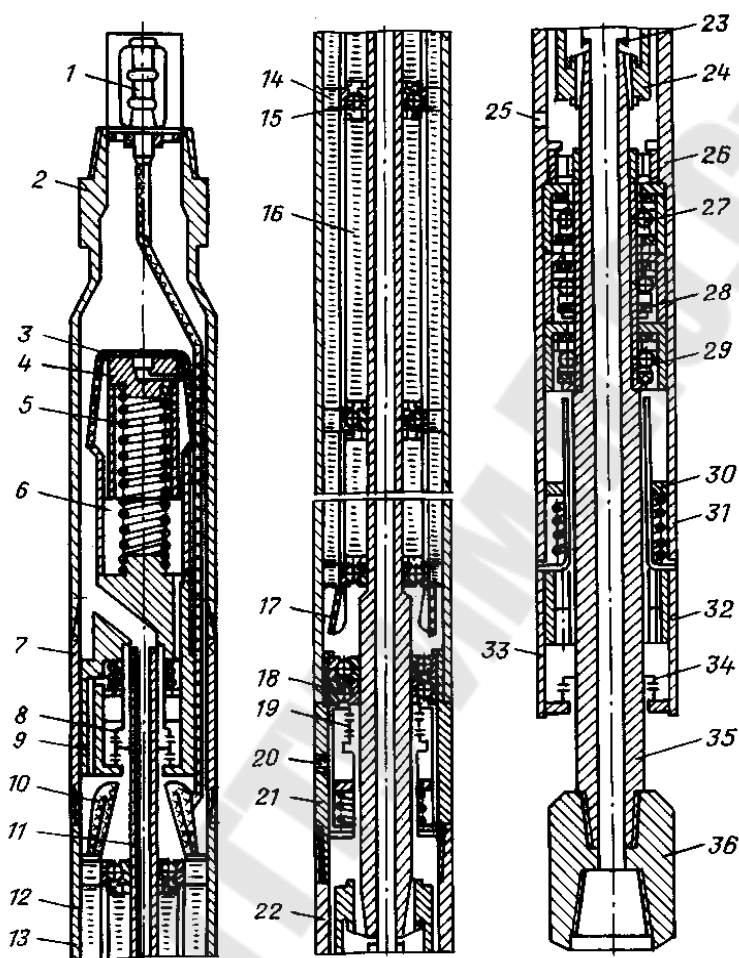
Конструкция электробура: 1 – контактный стержень; 2 – переводник; 3 – резиновая диафрагма компенсатора двигателя; 4, 30 – поршень компенсатора двигателя и шпинделя соответственно; 5, 31 – пружина; 6 – цилиндр компенсатора; 7 – соединительный корпус двигателя; 8, 19 – верхний и нижний сальники двигателя; 9 – верхний клапан двигателя; 10, 17 – верхняя и нижняя части обмотки статора; 11 – вал двигателя; 12 – пакет магнитопроводной стали статора; 13 – корпус статора; 14 – промежуточный пакет статора из немагнитного материала; 15, 18 – промежуточный и нижний подшипники двигателя; 16 – секция ротора двигателя; 20 – клапан; 21 – нижний соединительный корпус; 22 – корпус шпинделя; 23 – втулка; 24 – зубчатая муфта; 25 – клапан; 26, 32 – верхний и нижний радиальные подшипники; 27 – упорный подшипник; 28, 29 – наружная и внутренняя обоймы распределителя осевой нагрузки; 33 – пробка; 34 – сальник шпинделя; 35 – вал шпинделя; 36 – переводник на долото
